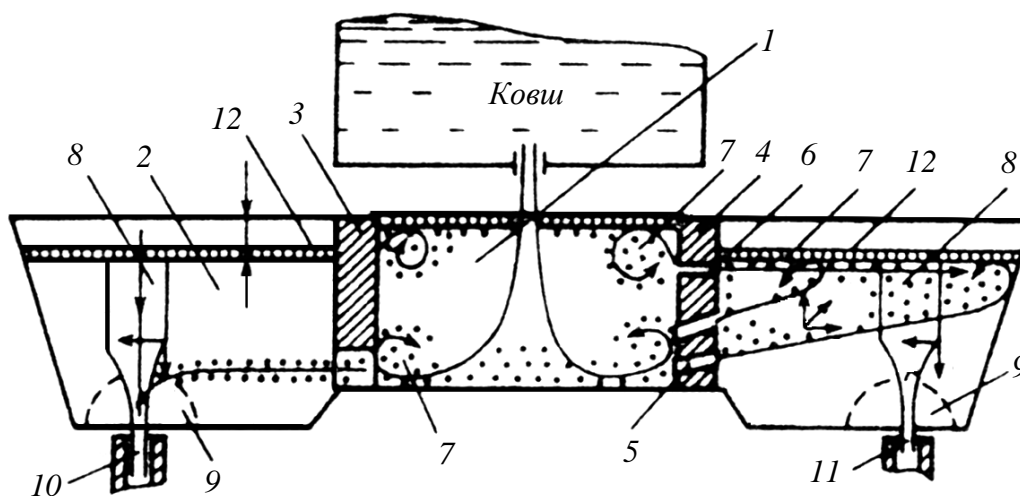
Схема работы промежуточного ковша: 1 и 2 – приемная и раздаточная камеры; 3 и 4 – обычная и опытная перегородки; 5 и 6 – наклонный щелевидный и прямой цилиндрический каналы; 7 – скопление включений; 8 – зона взаимодействия разливочного стакана; 9 – зона затягивания; 10 и 11 – сравнительный и опытный ручки; 12 – шлак
